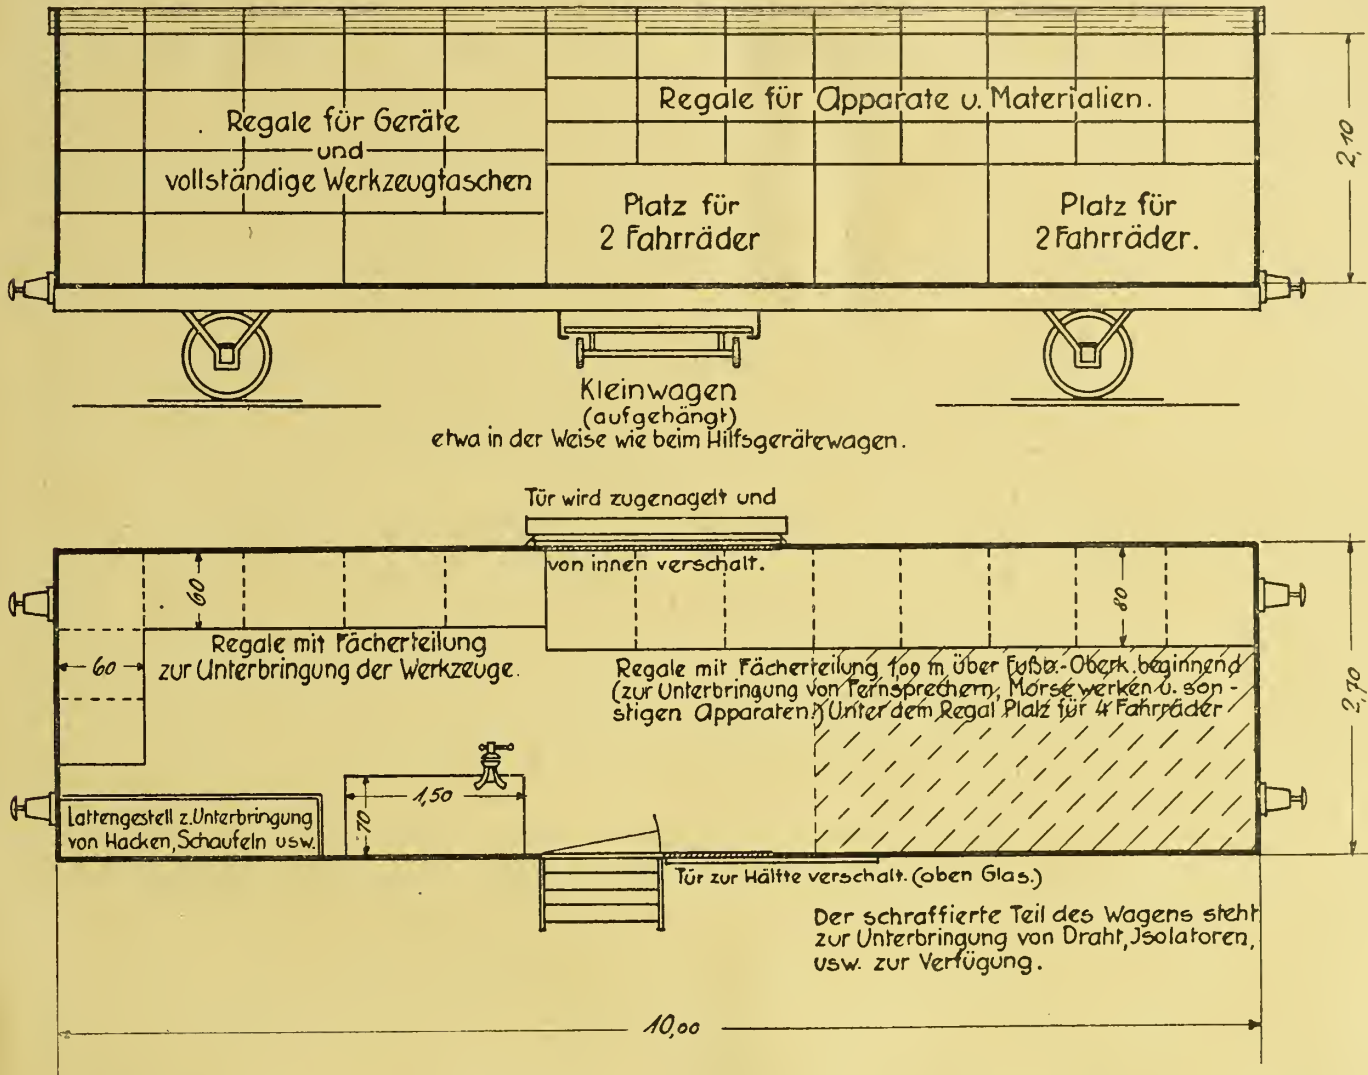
Werkzeugwagen für einen Telegraphenbautrupp.
